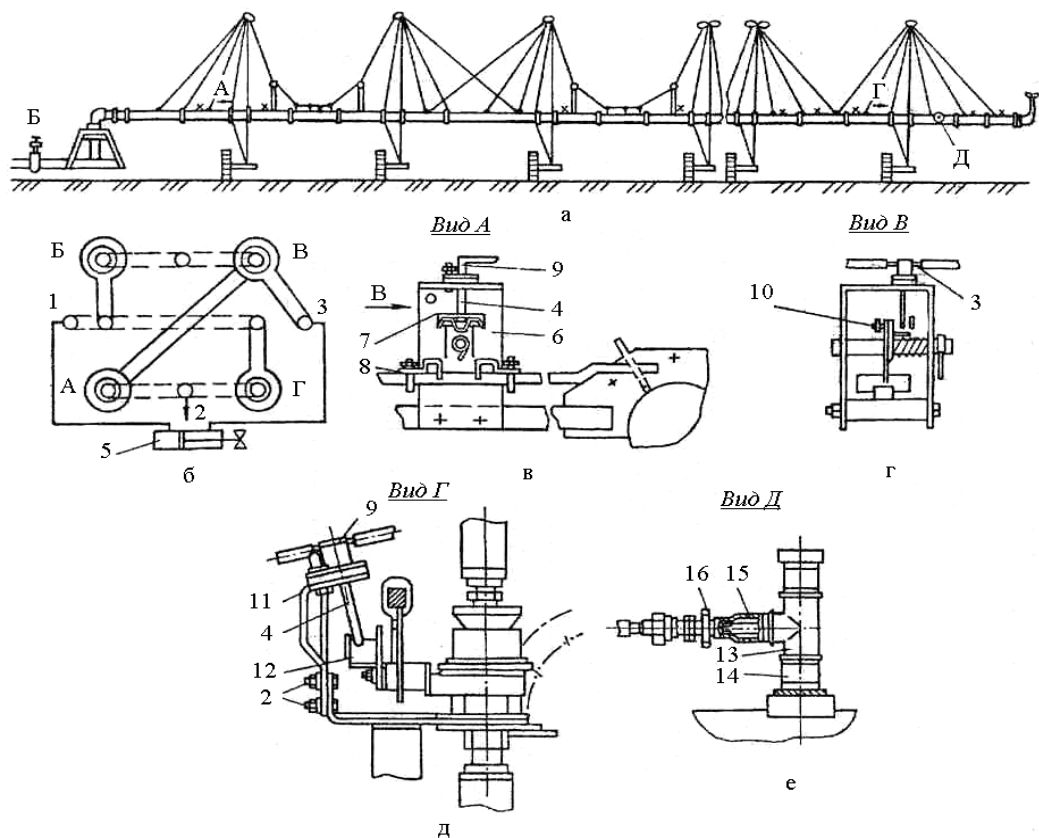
Система гидравлической аварийной защиты ДМ «Фрегат».
